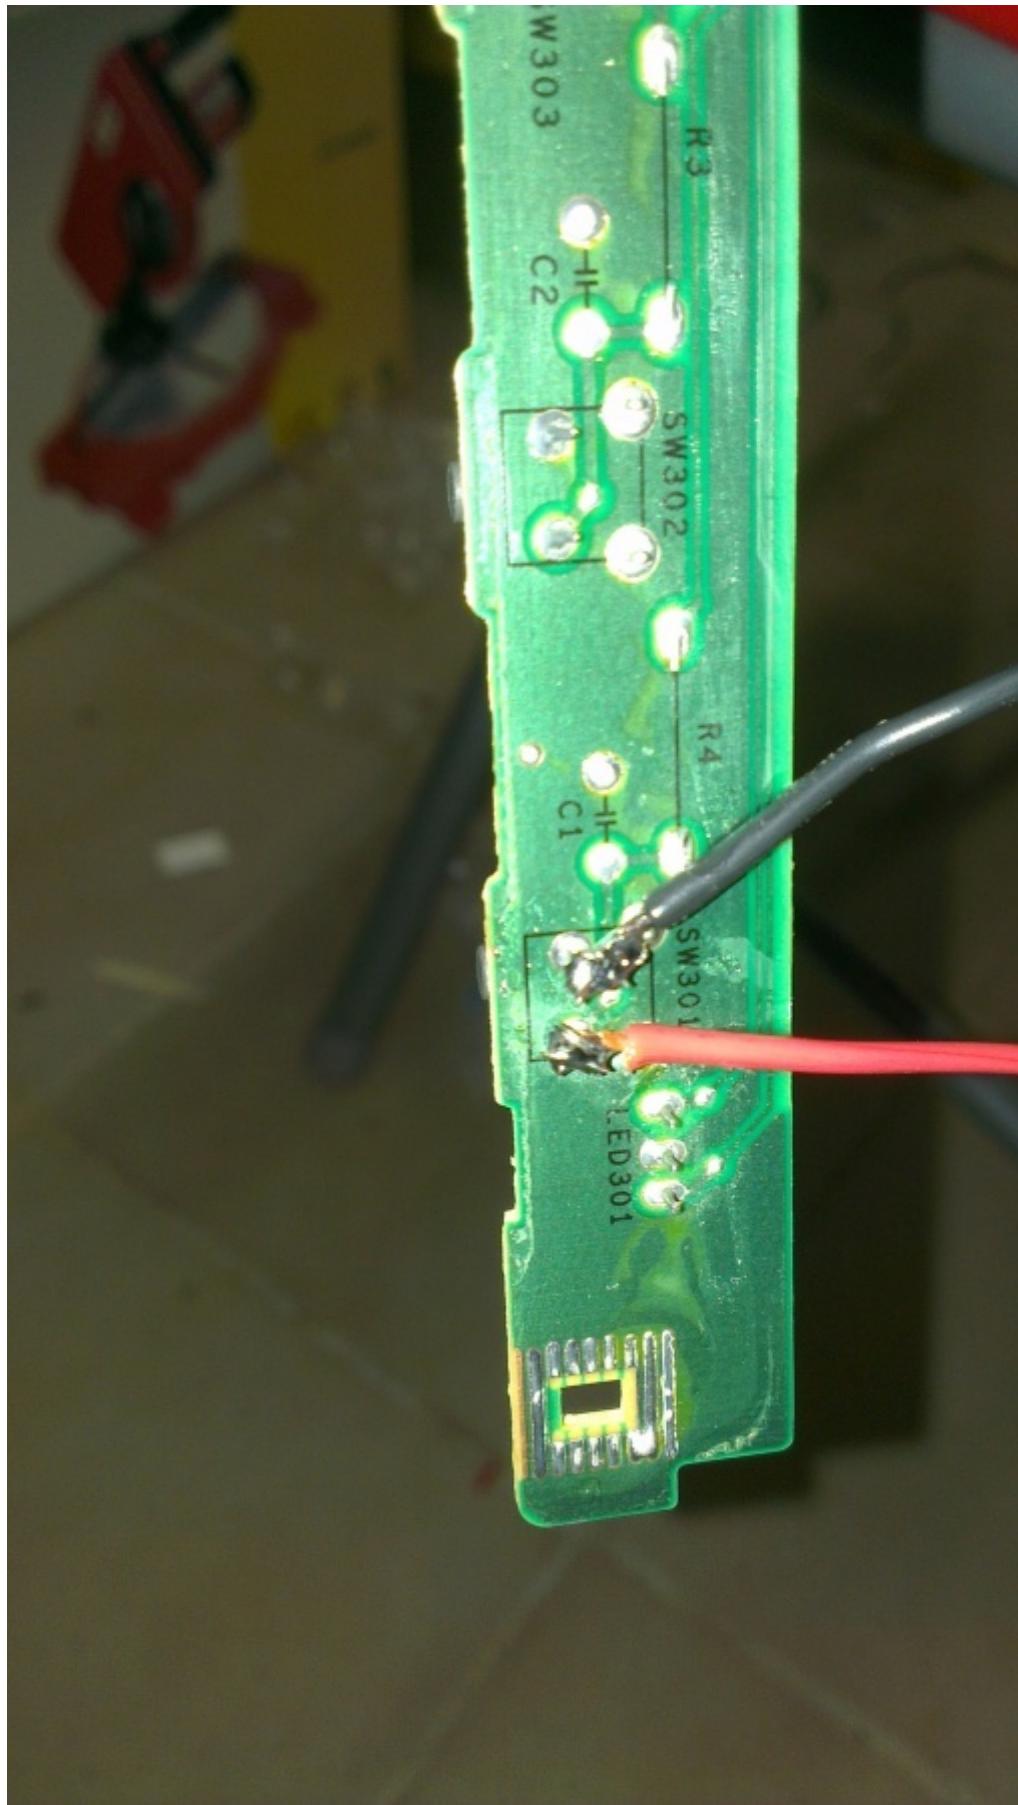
Detalle de la botonera con los 2 cables soldados
